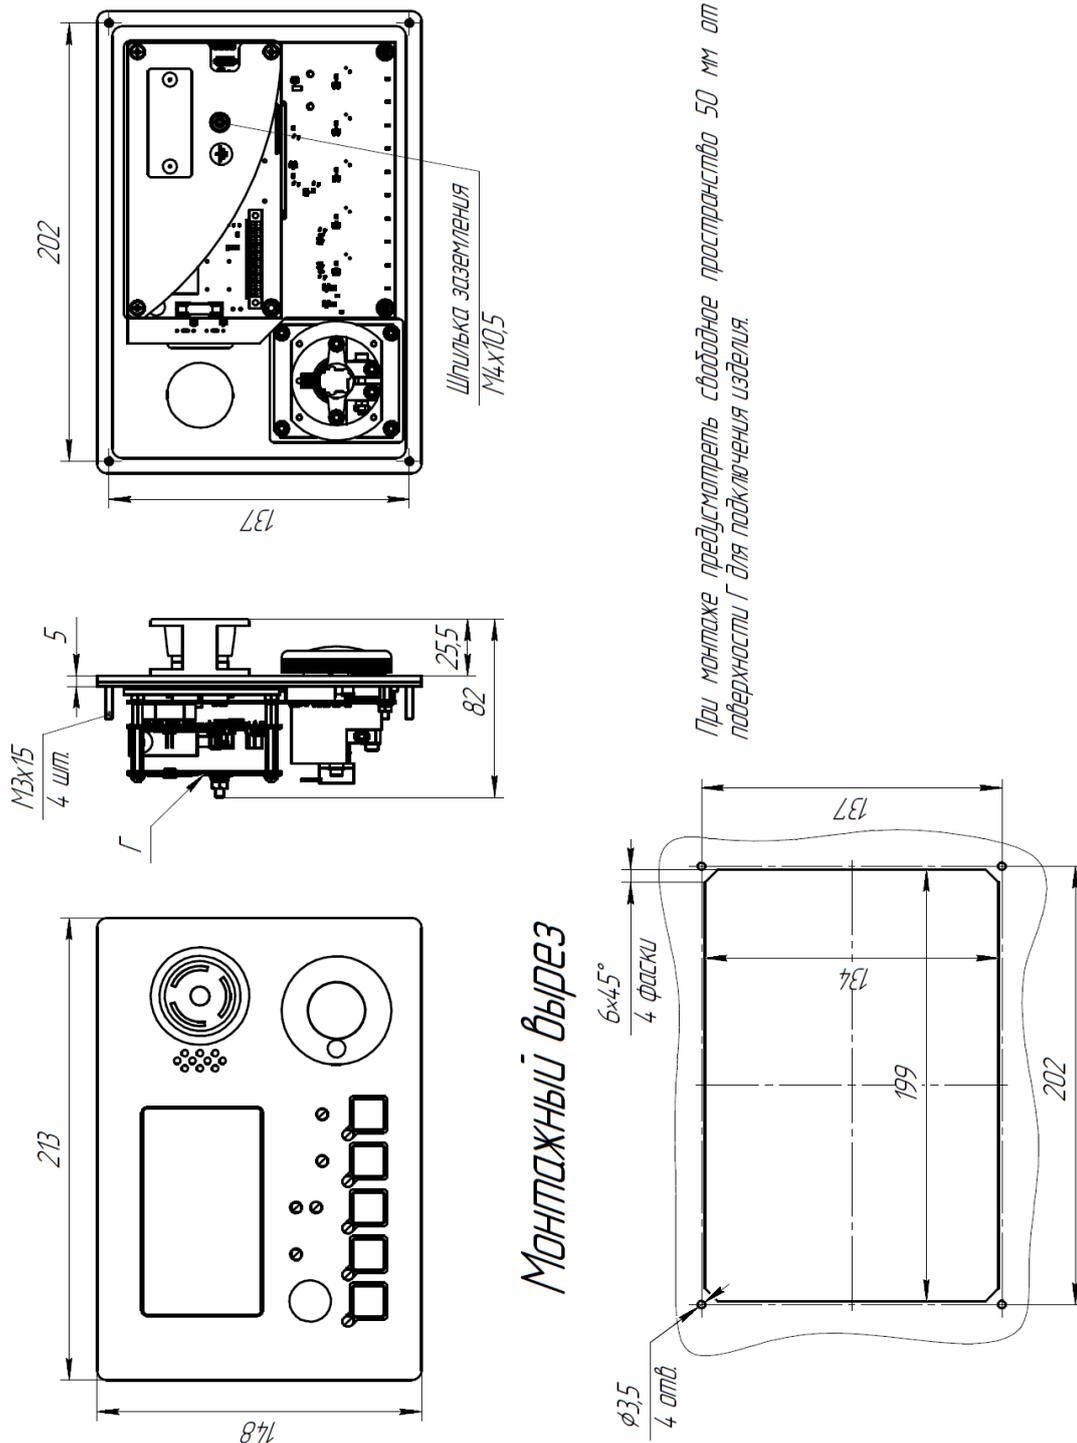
Габаритные и установочные размеры ПДУ-К (с ручкой)
